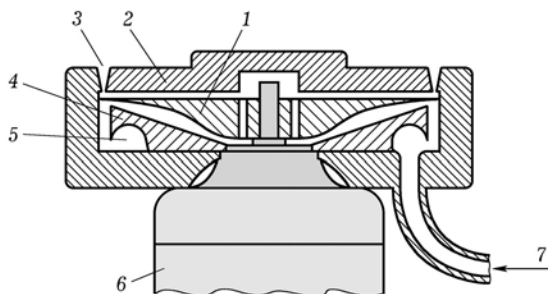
Устройство сирены: 1 — ротор; 2 — статор; 3 — отверстия в статоре; 4 — отклоняющая пластина; 5 — воздушная камера; 6 — электромотор; 7 — сжатый воздух
